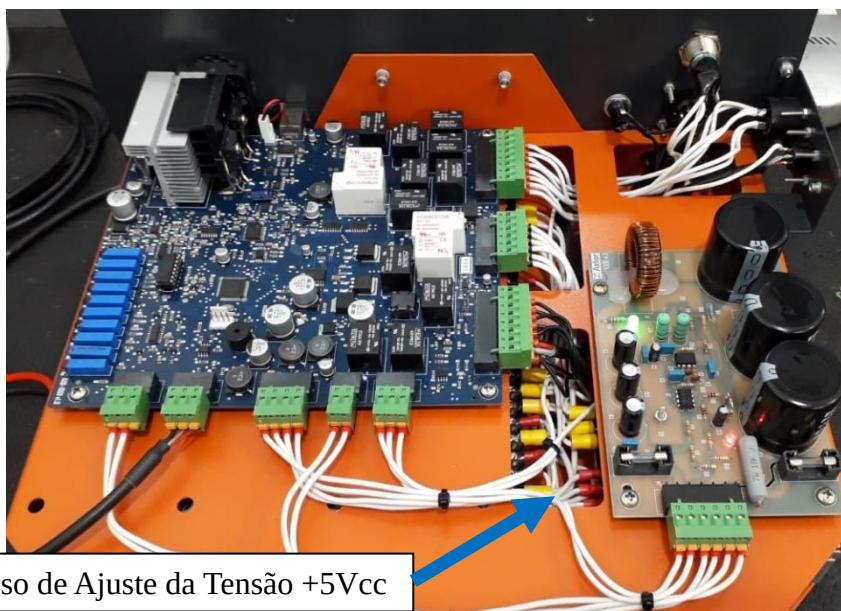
Montagem da Placa AXD1001 e FV300 no CHASSI
